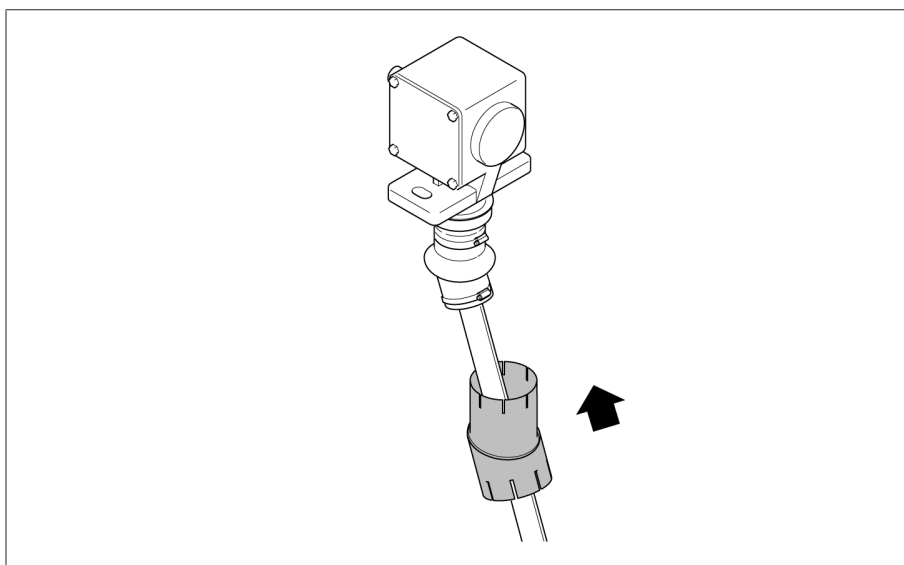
Glisser le tube de protection rotatif par-dessus le tube carré
